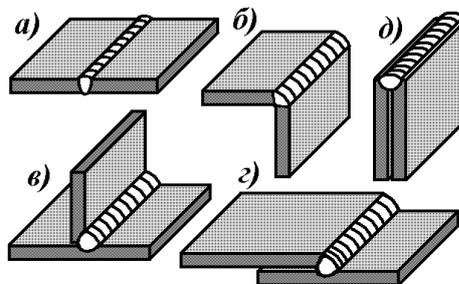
Типы сварных соединений: а) стыковое; б) угловое; в) тавровое; г) нахлесточное; д) торцовое
